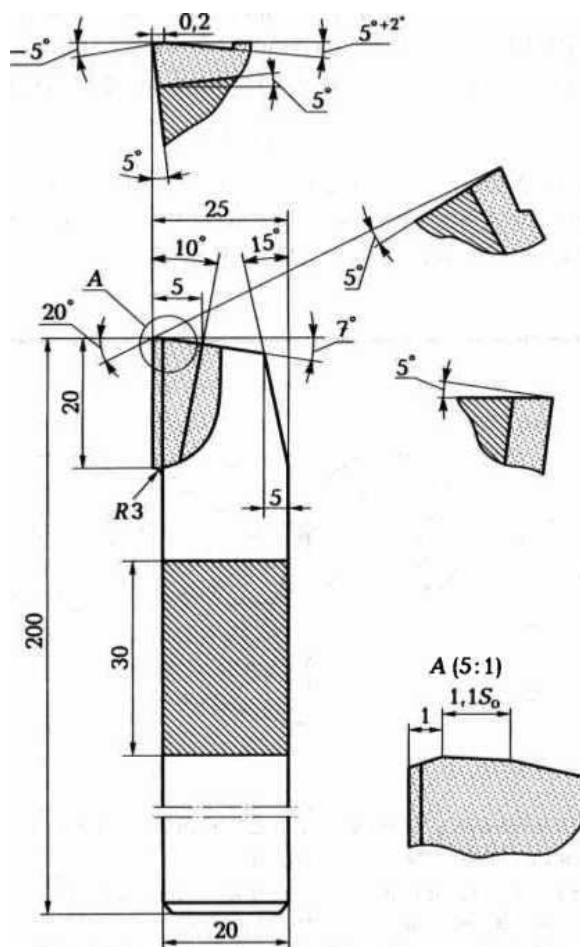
Проходной упорный резец конструкции Колесова.
